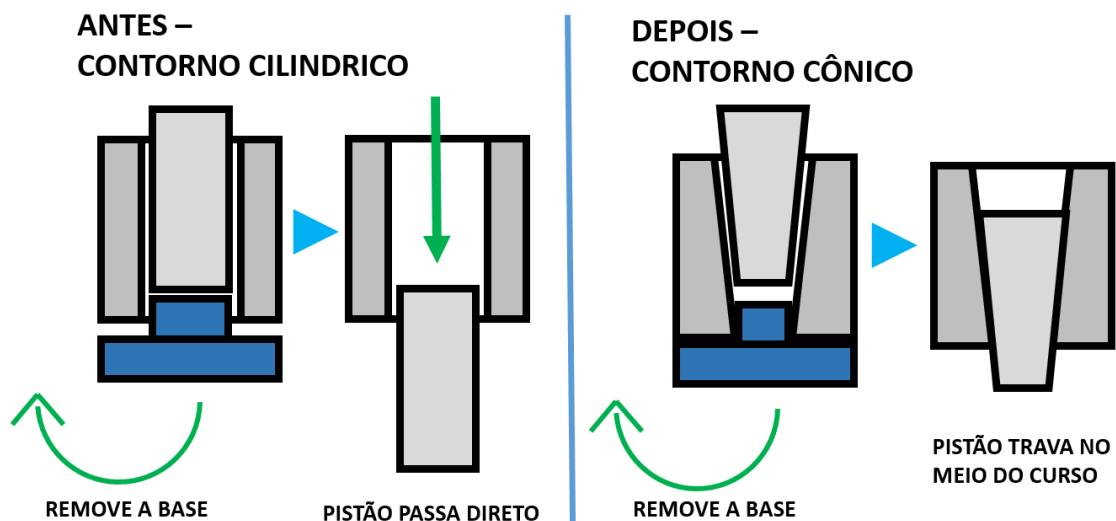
Sequência de encaixe do molde cilíndrico (A e B)
